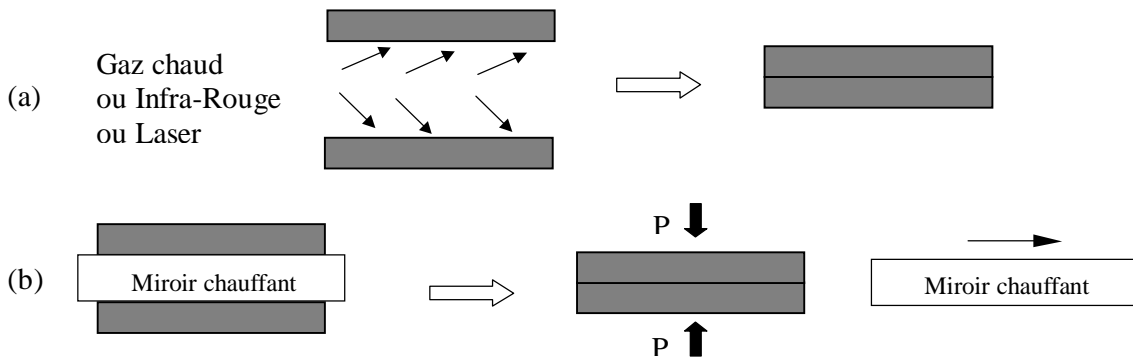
3 : Représentation schématique du soudage: (a) par gaz chaud, IR ou laser, (b) par miroir chauffant
